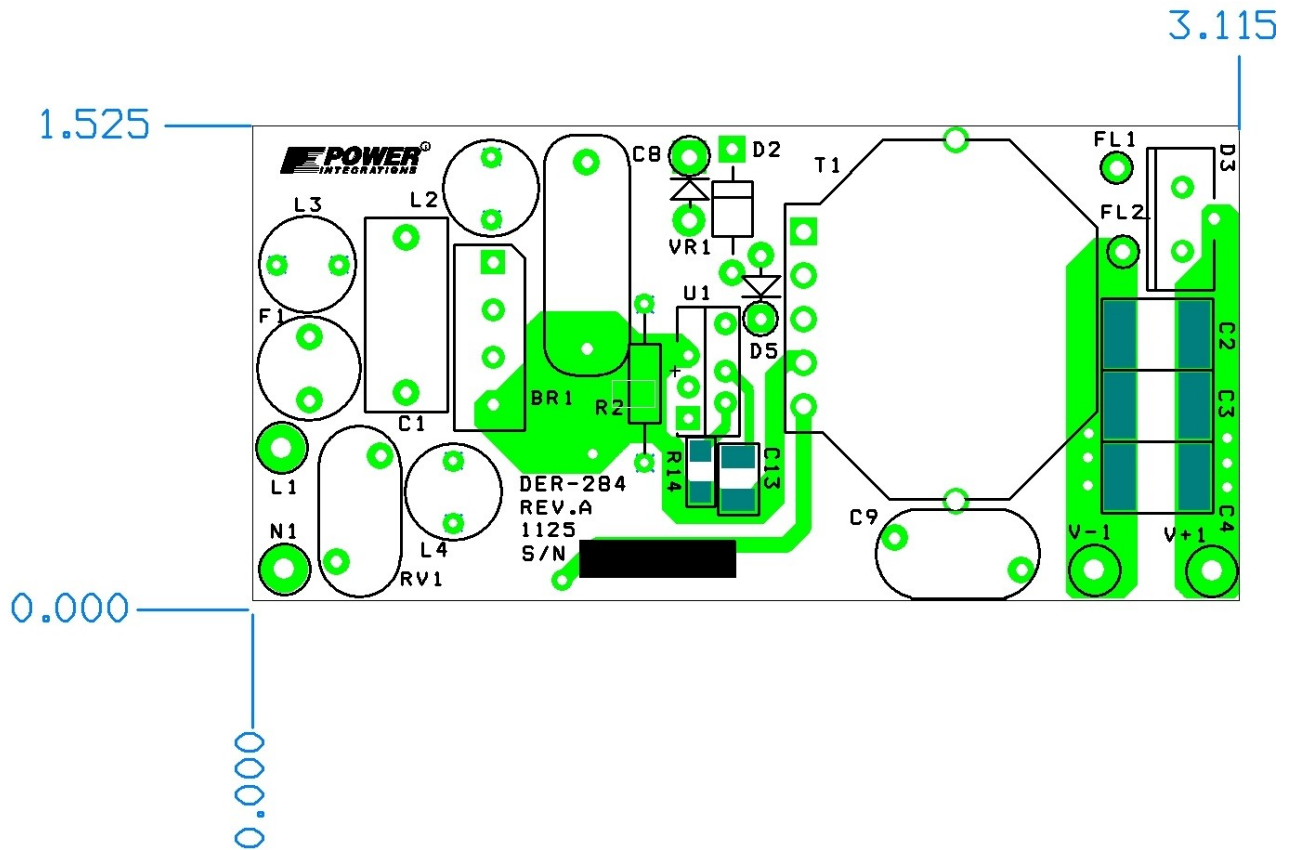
PCB DER-284 보드 레이아웃, Top 면
